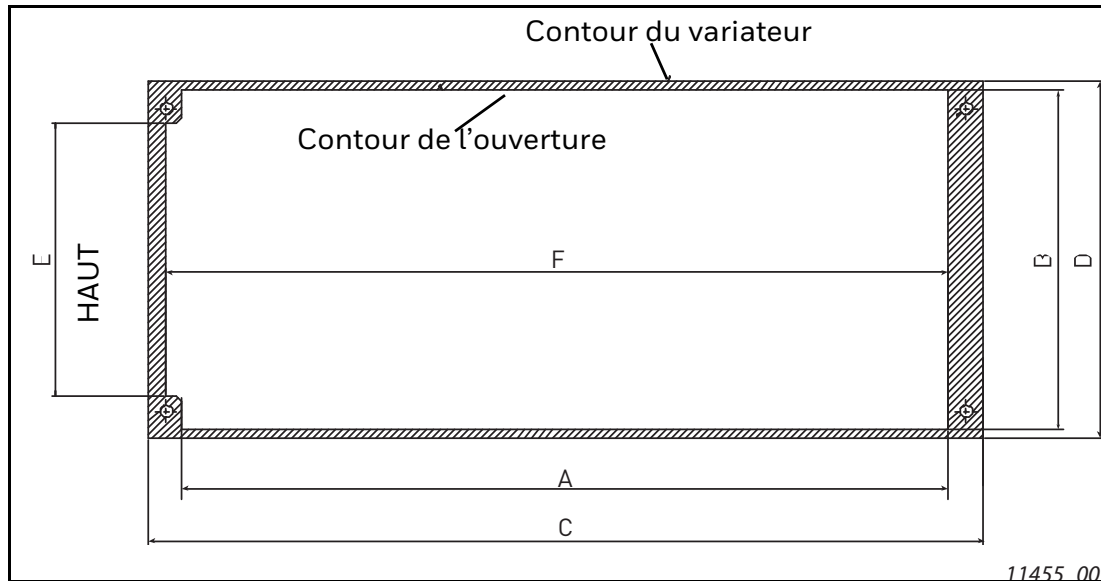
Dimensions de découpe de la bride pour châssis MR4 à MR6
